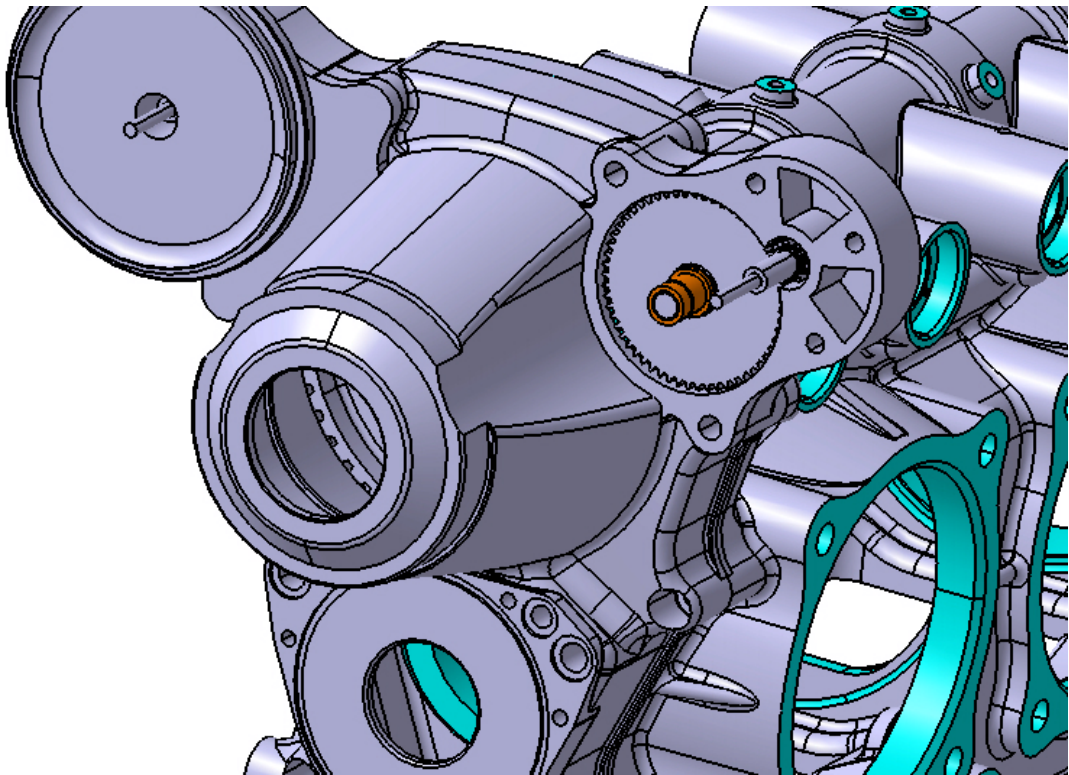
Particolare del gruppo moltiplicatore assemblato
